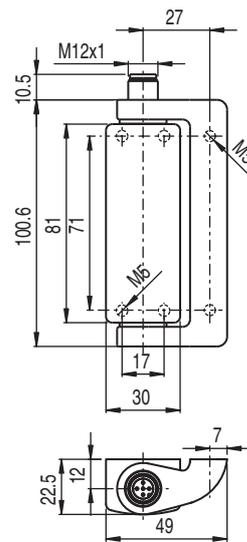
Dimensões do S400-M4M12-T em mm
